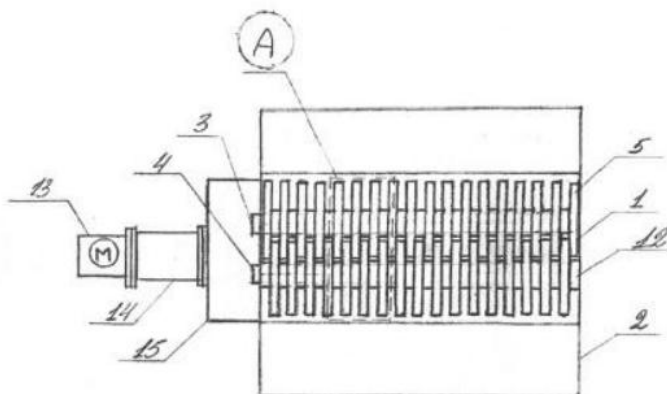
Загальний вид валкової дробарки (вид зверху) [2]
